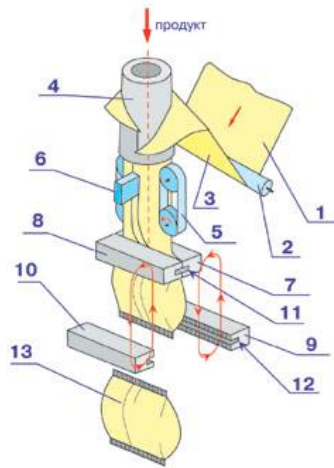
Компонування машини з парними губками зварювання: 1, 3 – плівка; 2 – механізм натягу плівки; 4 – рукавотворювач; 5 – механізм протягування плівки; 6 – губка поздовжнього зварювання; 7, 8, 9, 10 – губки поперечного зварювання; 11, 12 – відрізний механізм; 13 – готовий пакет
